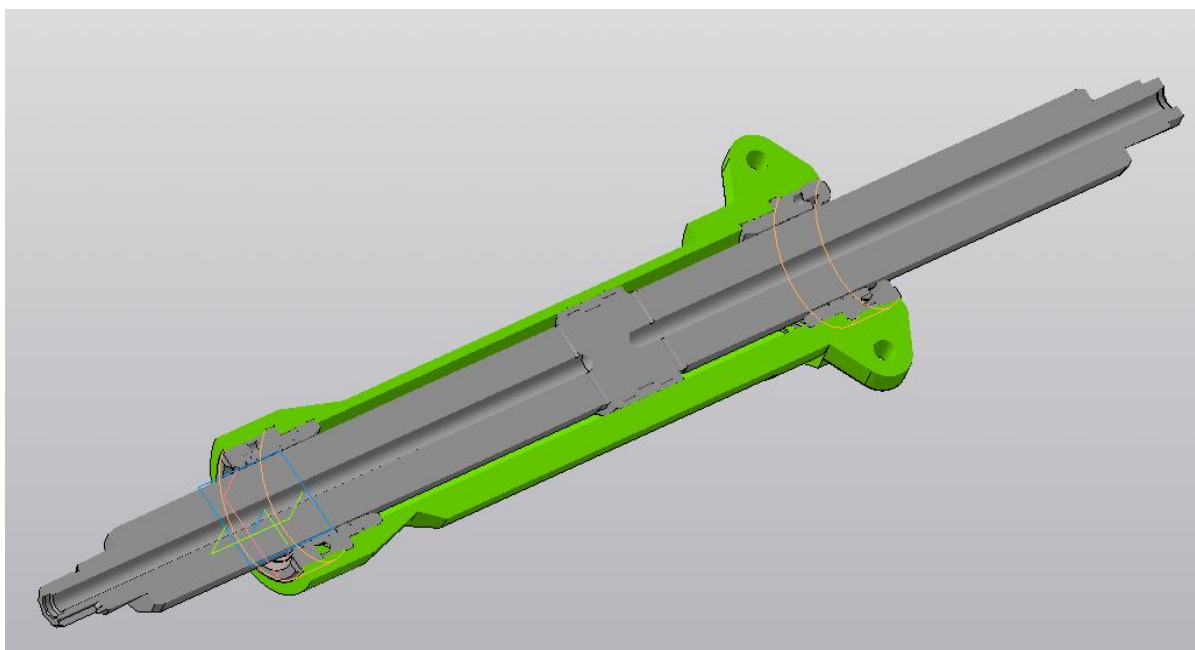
Общий вид гидроцилиндра с разрезом
